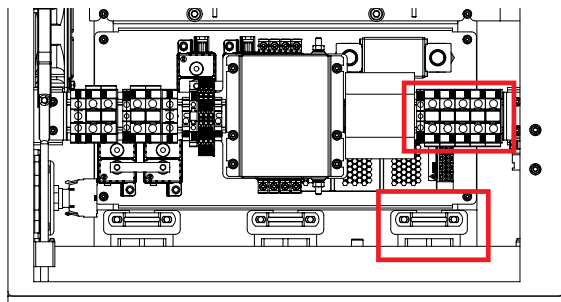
CABLAGEM DE ALIMENTAÇÃO DE CA
